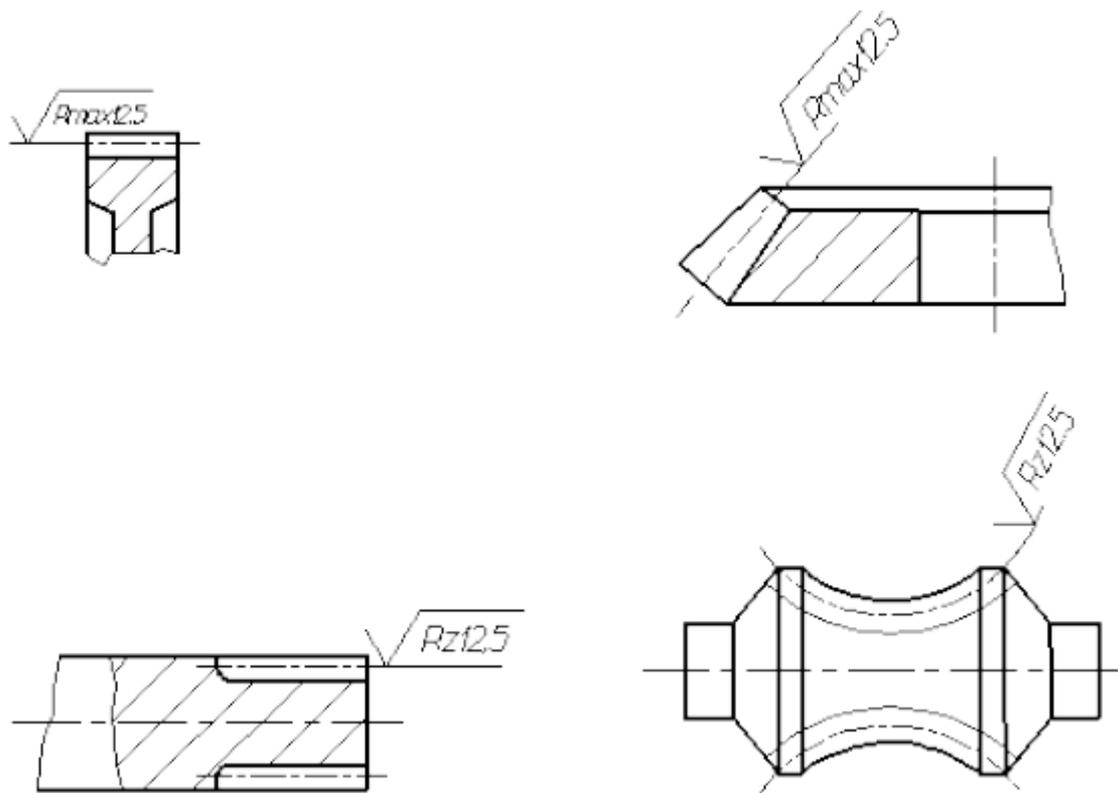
Примеры обозначения шероховатости рабочих поверхностей зубьев
